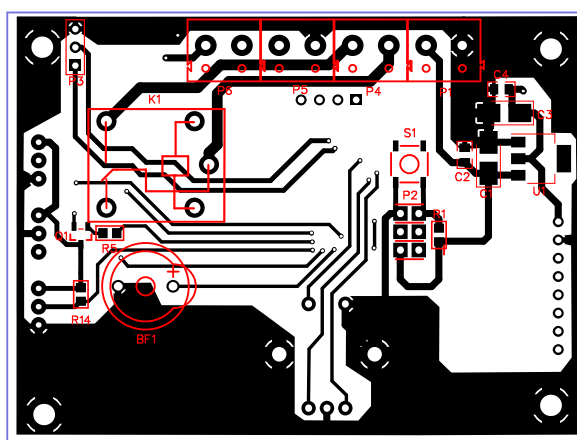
Монтажна схема нижнього шару друкованої плати
